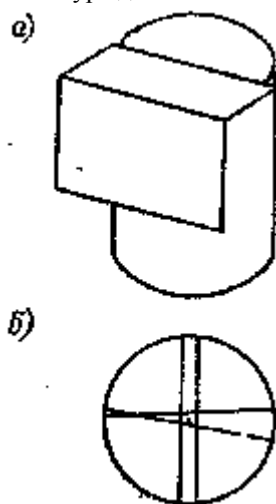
Разметка центрального отверстия в торце цилиндрической детали: а — приспособление для разметки; б — положение разметочных линий относительно центра
